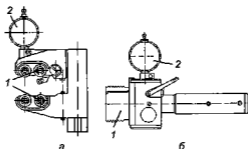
Схемы индикаторных приборов для измерения наружной (а) и внутренней (б) резьб: 1 – резьбовые измерительные элементы; 2 – отсчетное устройство
